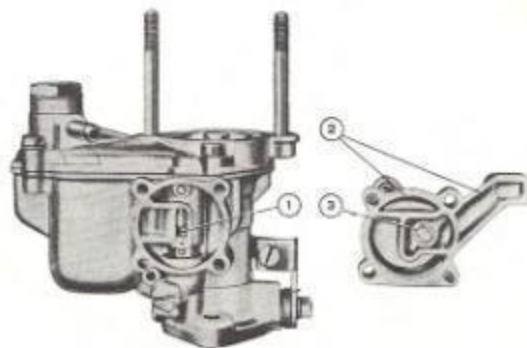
WEBER karburator type 26 IMB 1 med aftaget starteranordning.
